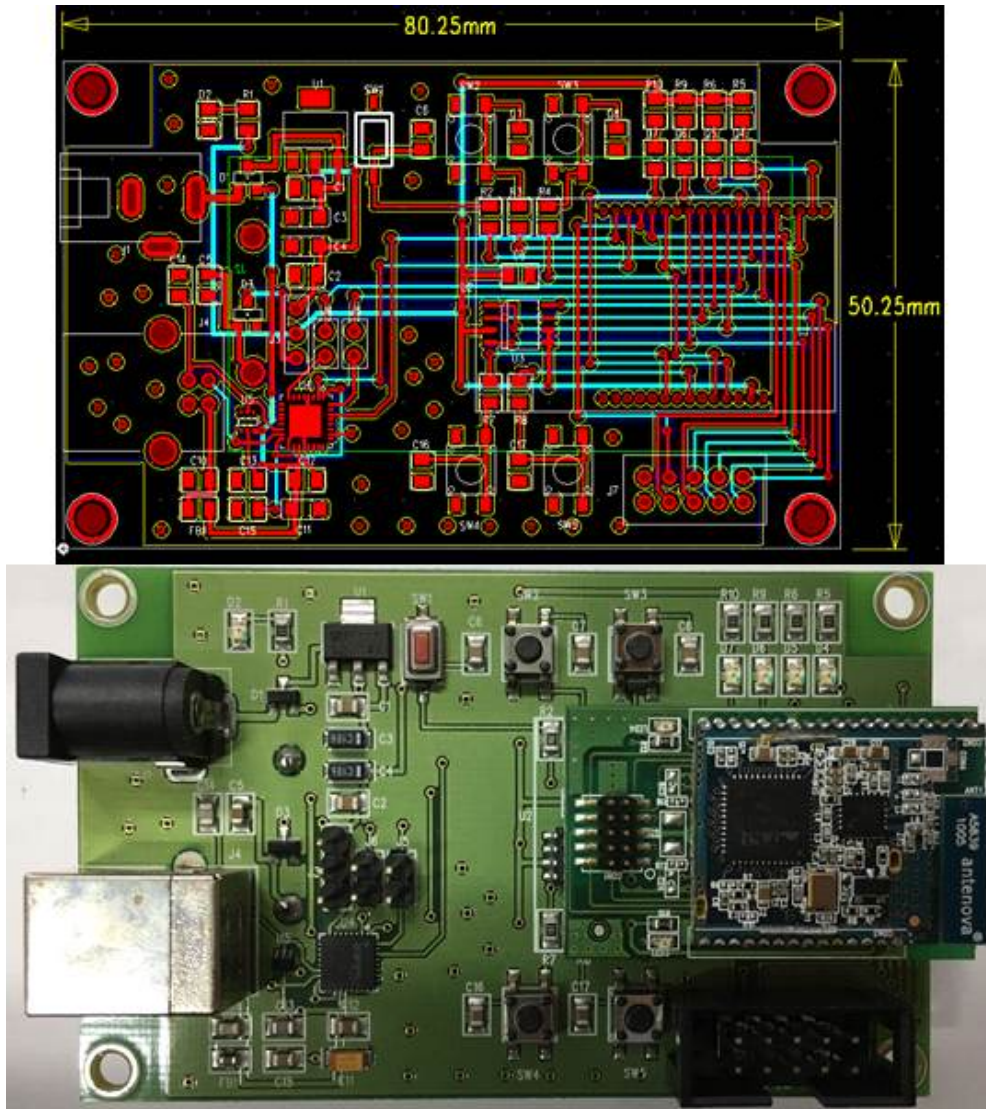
진동현 타입 센서 PCB 설계 파일 및 시작품
